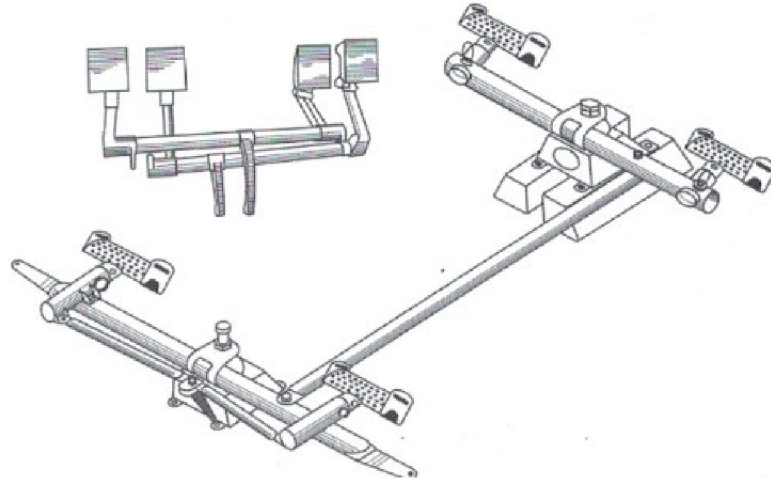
Sústava hydraulického riadenia brzd (upravené) [13]
